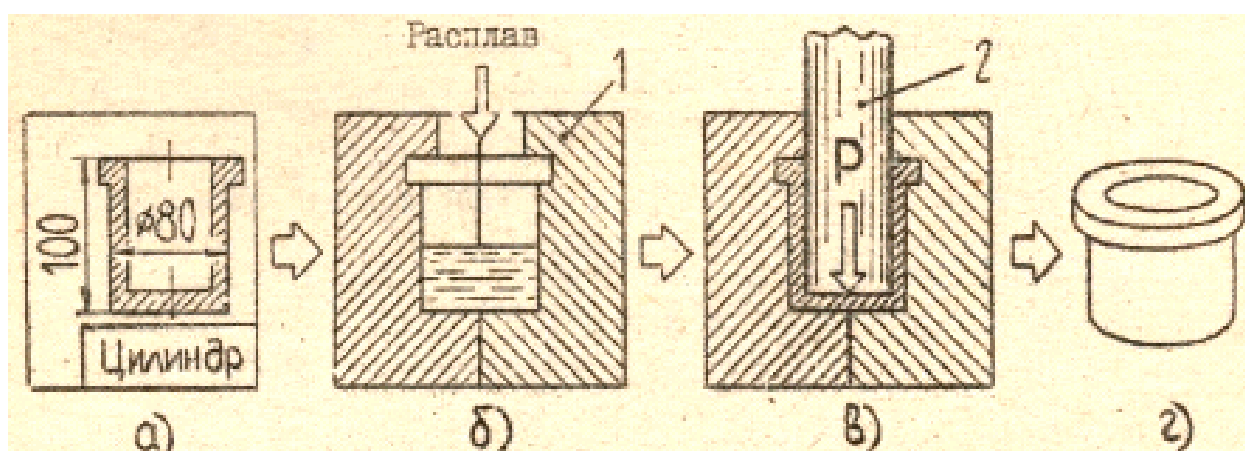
Штамповка жидкого металла: а — чертеж изделия; б — заливка расплава; в — штамповка; г — изделие; 1 — разъемная матрица; 2 — пуансон
